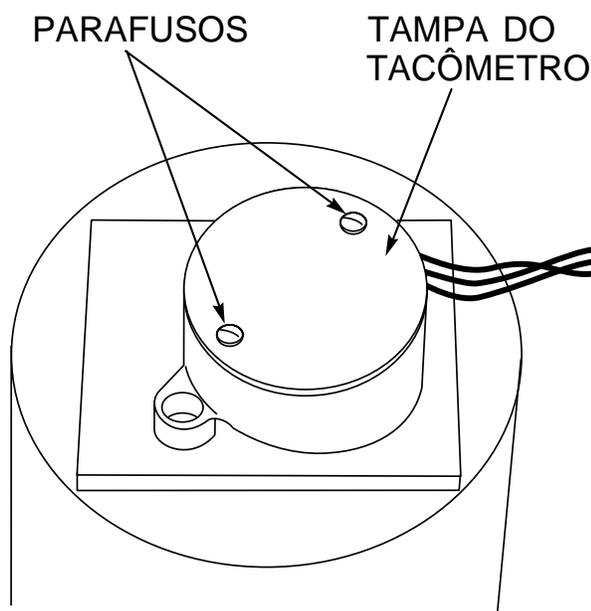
CONJUNTO DO SENSOR E TAMPA
